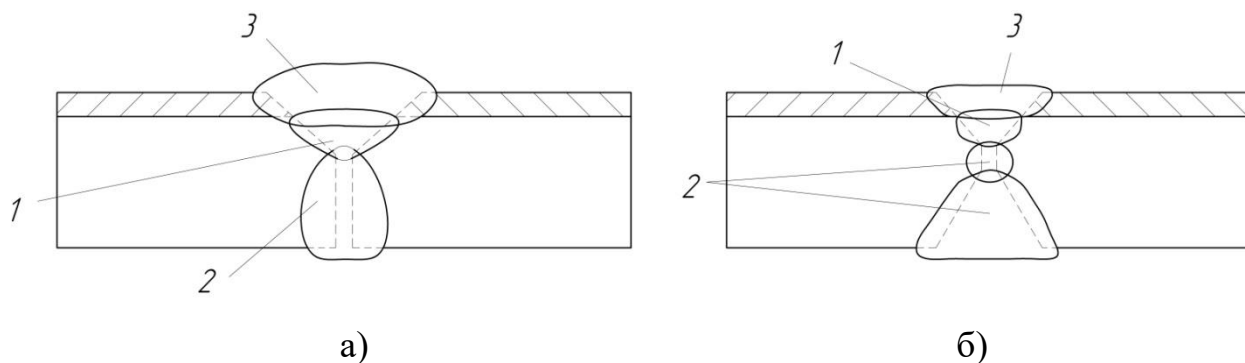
Последовательность сварки листов двухслойных сталей
